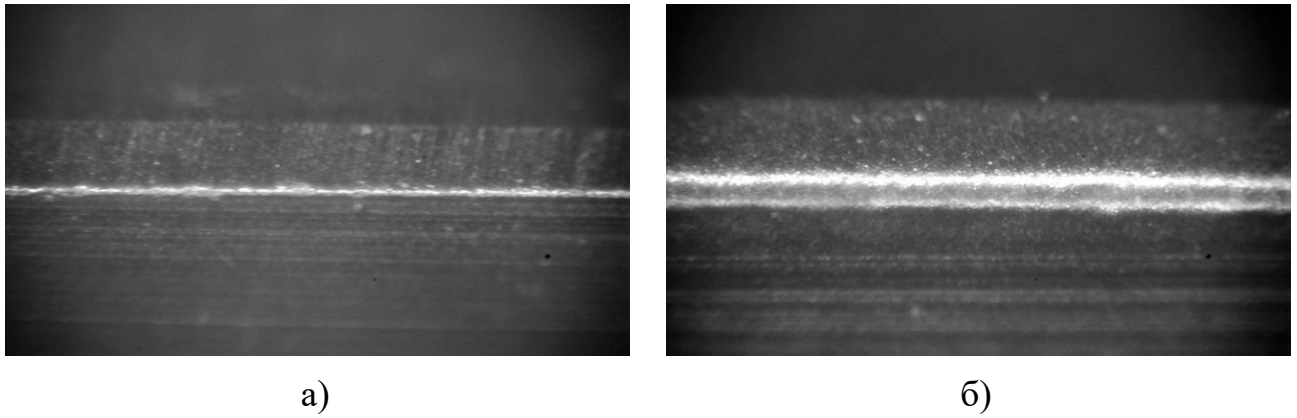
Скругление режущей кромки ρ : а) инструмент с острой кромкой, б) инструмент со скругленной кромкой
